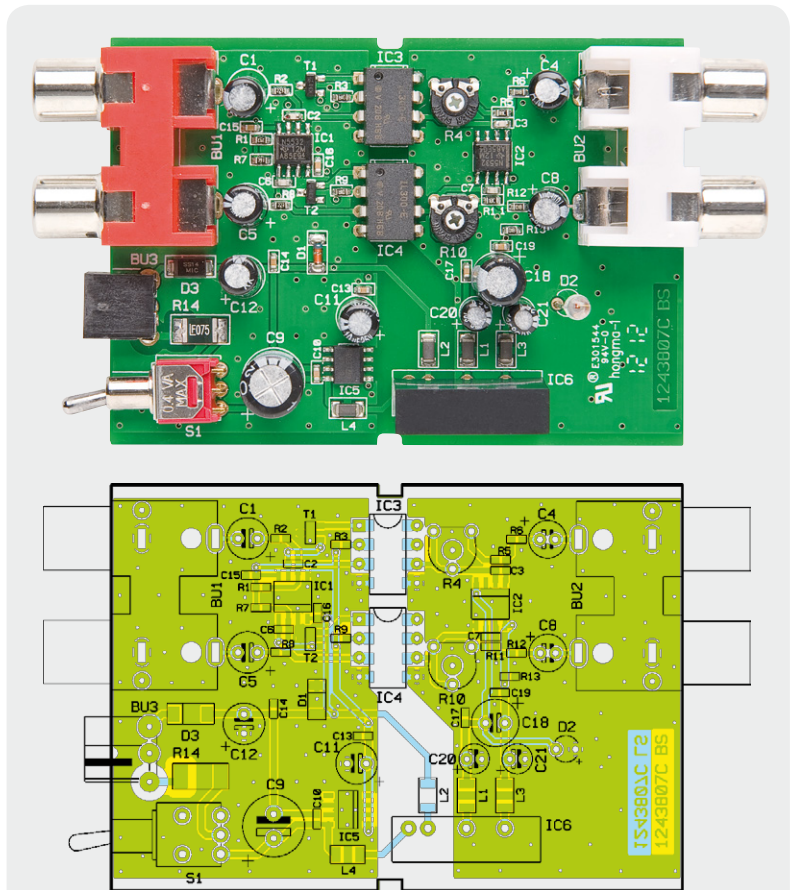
Fertig aufgebaute Platine des OTV100 mit Bestückungsplan
